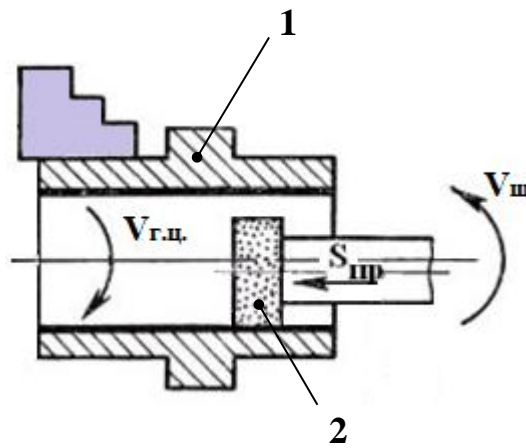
Схема щеточної обробки напильної поверхні:
